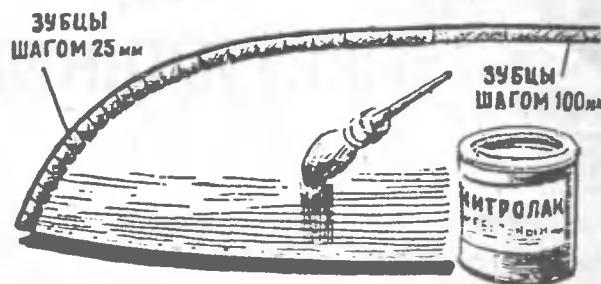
Оклейка тканью готового корпуса с обшивкой из крафт-бумаги.
